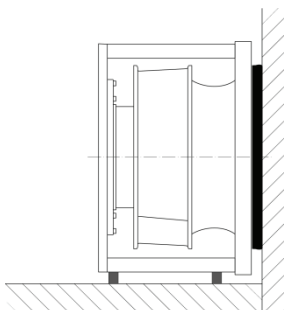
Вид RadiPac со стороны впуска с уплотнительным материалом
